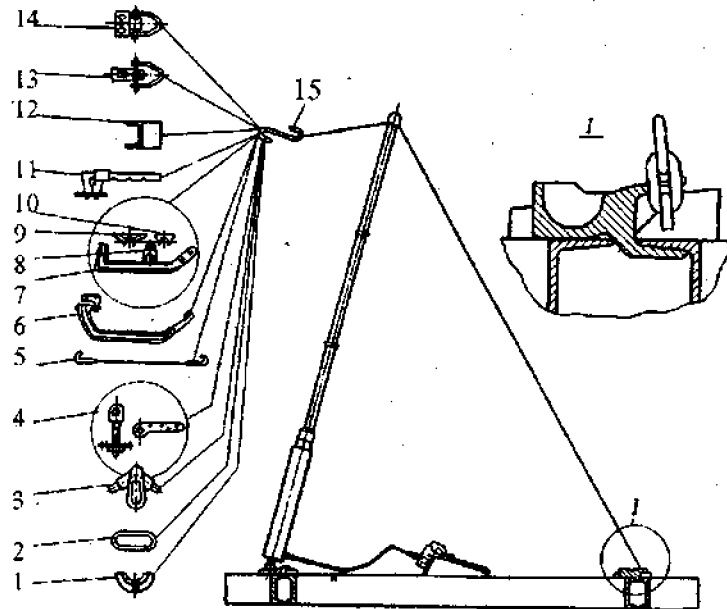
Варианты крепления приспособлений на силовой стойке стэнда Р-620:
